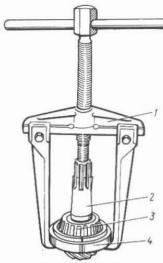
Desmontaje del aro interior del cojinete trasero del piñón de ataque con el extractor universal A.40005/1/7:
